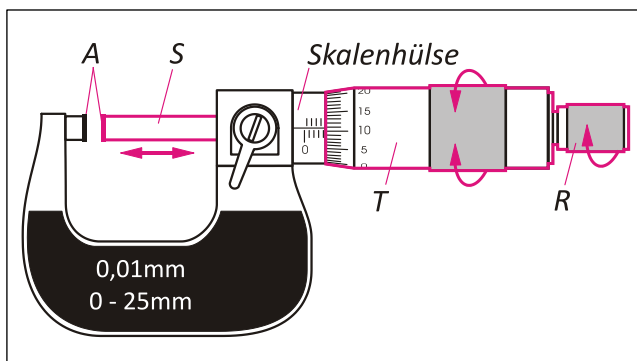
Prinzipskizze einer Bügelmessschraube
